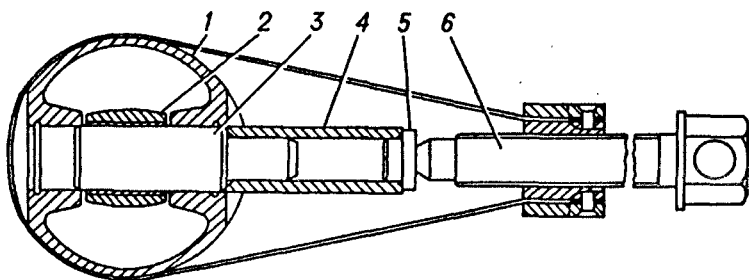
Запрессовка поршневого пальца в поршень и шатун с помощью приспособления 6999-7678:
